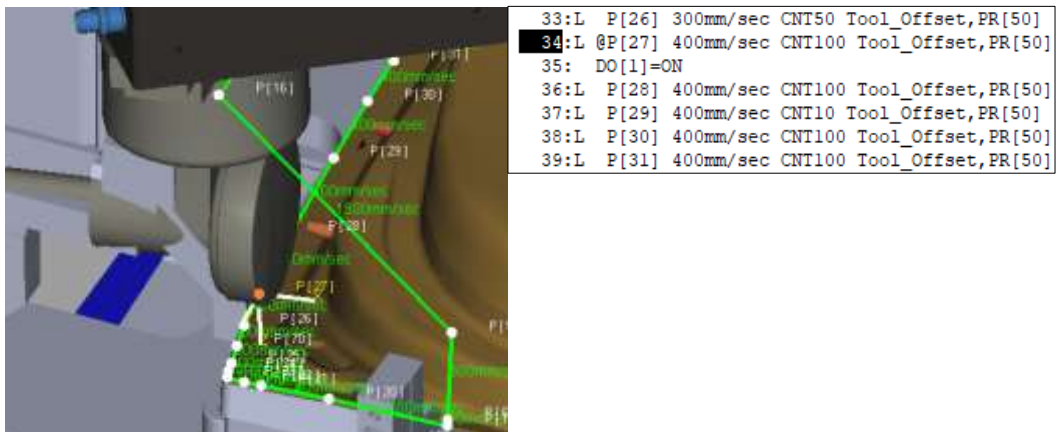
Robot C aproximación a la pieza para el engrapado de la esquina
